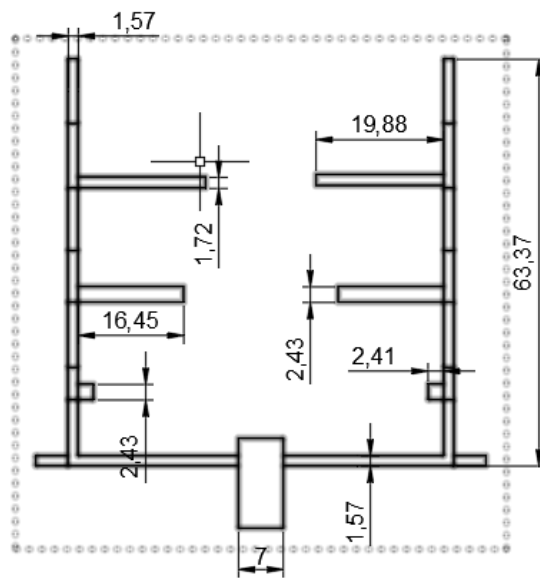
Esquema con dimensiones (cm) del sistema de colada propuesto. Vista superior.
